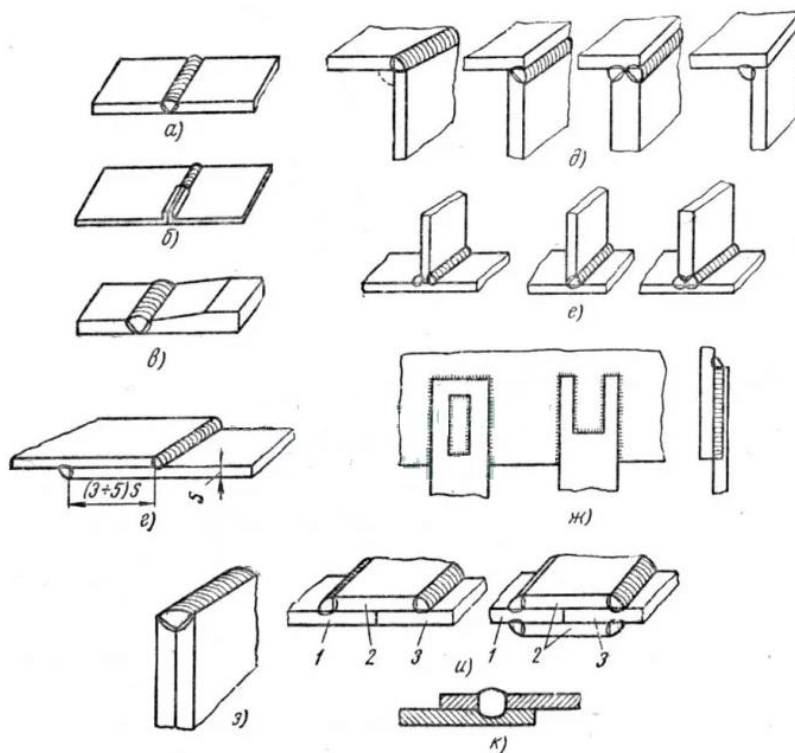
Основные виды сварных соединений:
